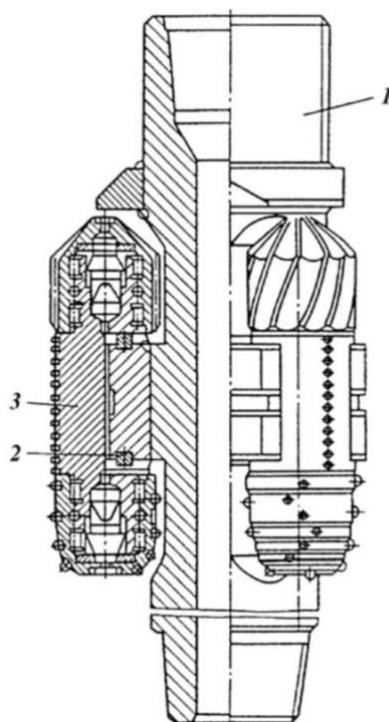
шарошечный калибратор типа КШУ: 1 – корпус; 2 – клинья; 3 – узел калибрующий
